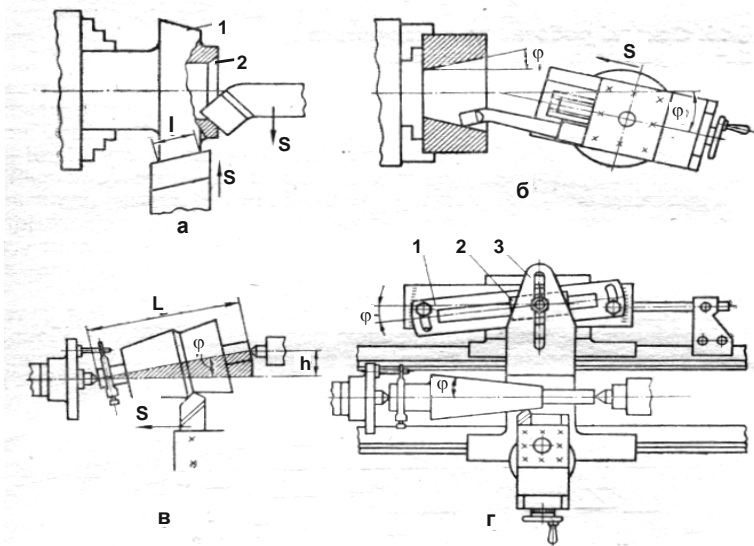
Обробка конічних поверхонь на токарному верстаті
